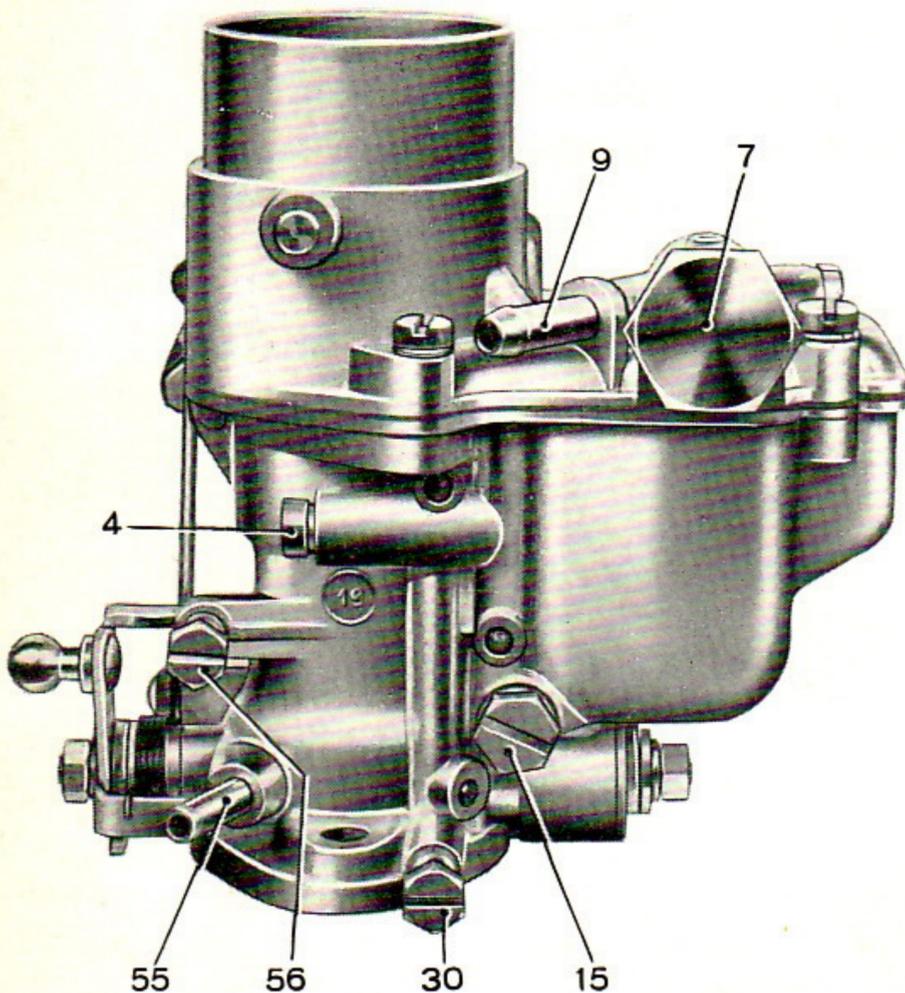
Carburatore dalla parte ingresso carburante, dei getti e della vite registro andatura minimo.
